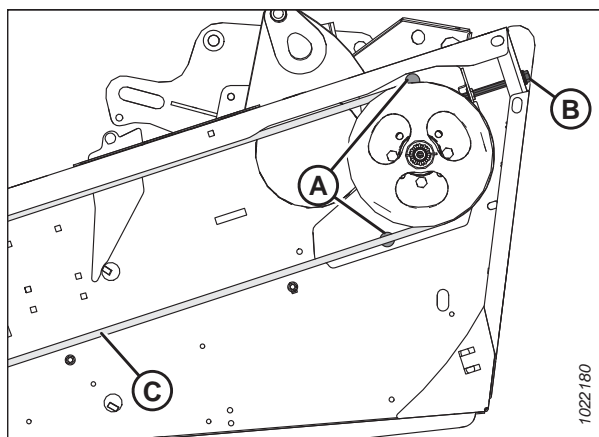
Привод и регулировочное приспособление ножа гидромотора
